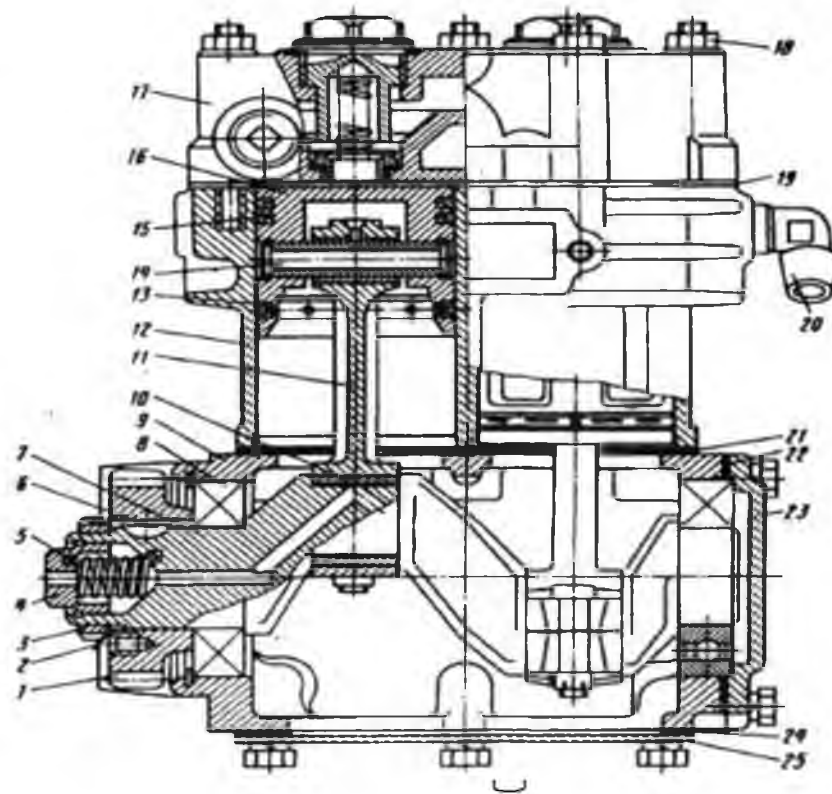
Загальний вигляд компресора автомобіля КамАЗ:
